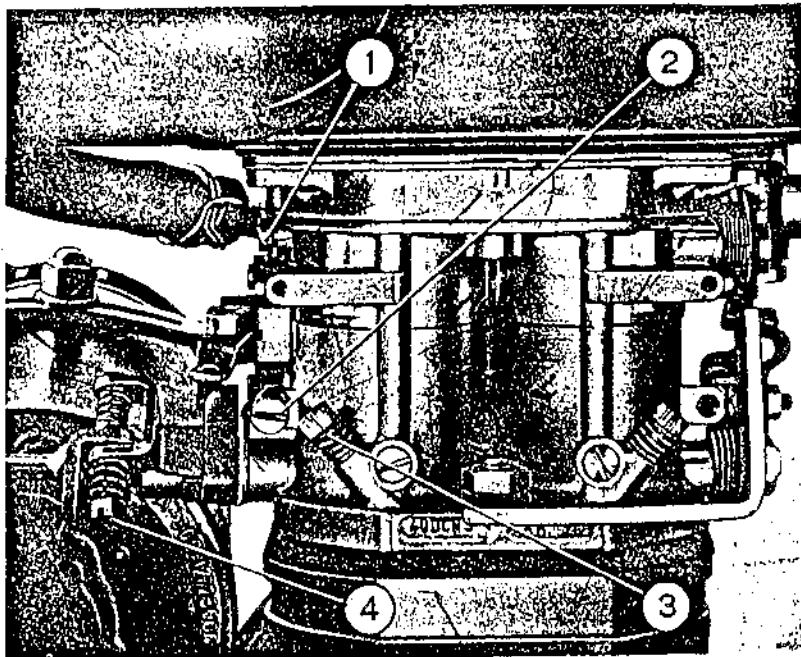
/01 - Réglage du ralenti (Carburateur Weber 40 DCN 4)
